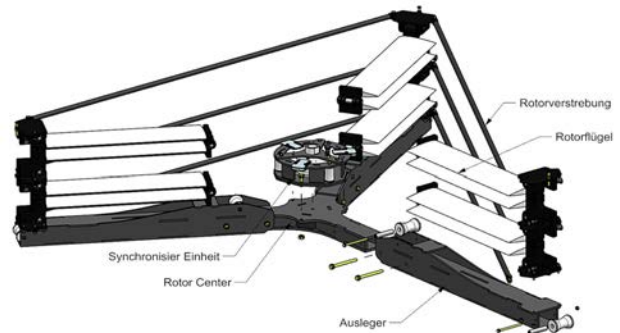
Explosionszeichnung des Rotoraufbaukonzeptes
